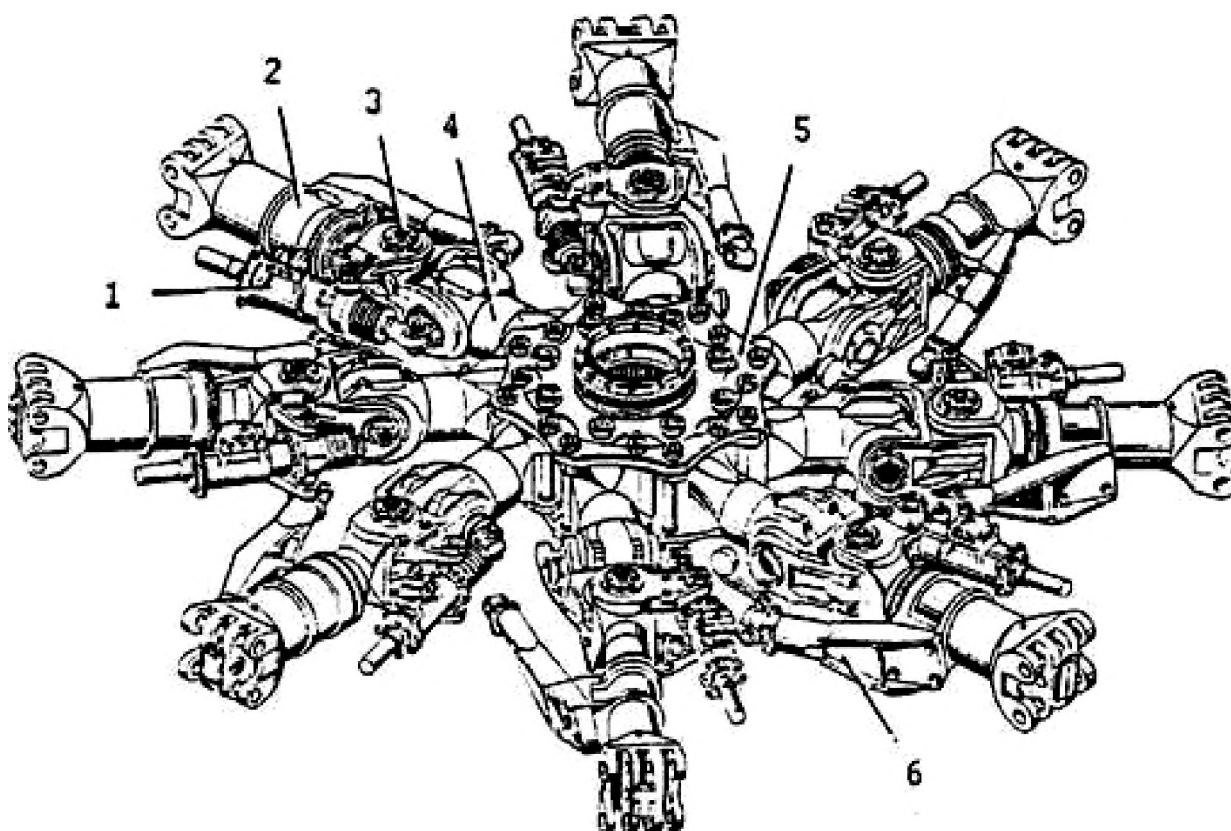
Элементы шарнирной втулки НВ вертолета Ми-26 [9]:
